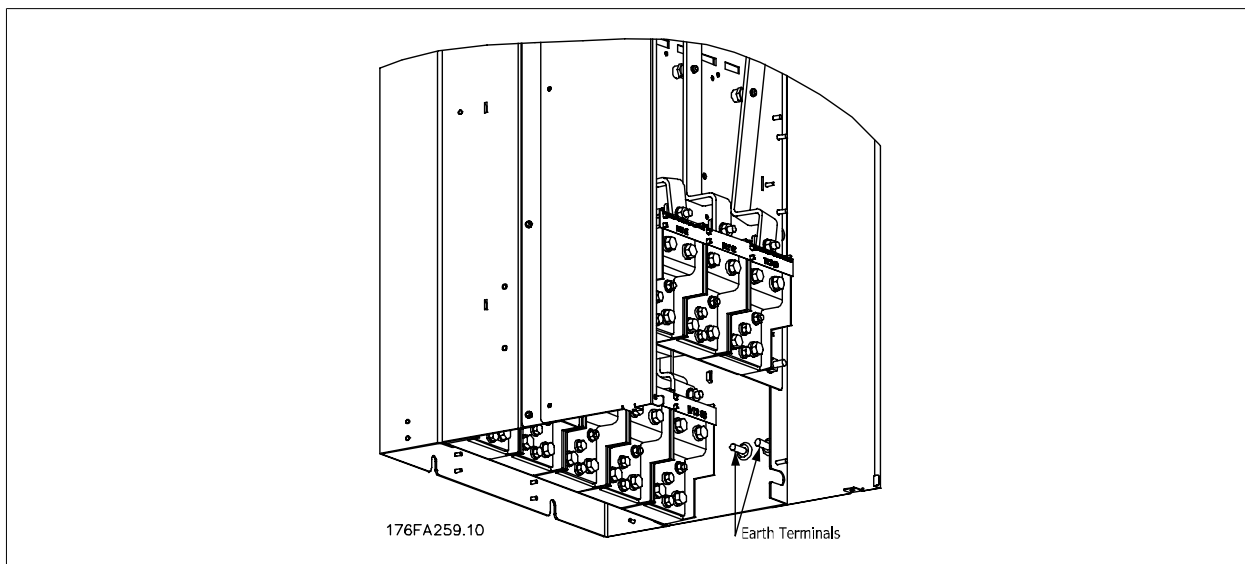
Расположение клемм заземления, IP00, корпуса E
